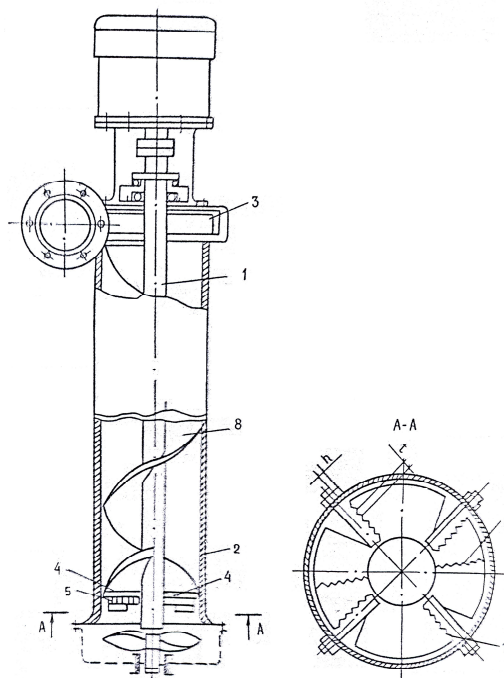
Насос с измельчающим устройством в виде зубьев, установленных на вращающихся и неподвижных ножах (1 – вал; 2 – корпус; 3 – рабочее колесо; 4 – вращающиеся ножи; 5 – неподвижный нож; 6-7 - режущие зубья; 8 - шнек).
